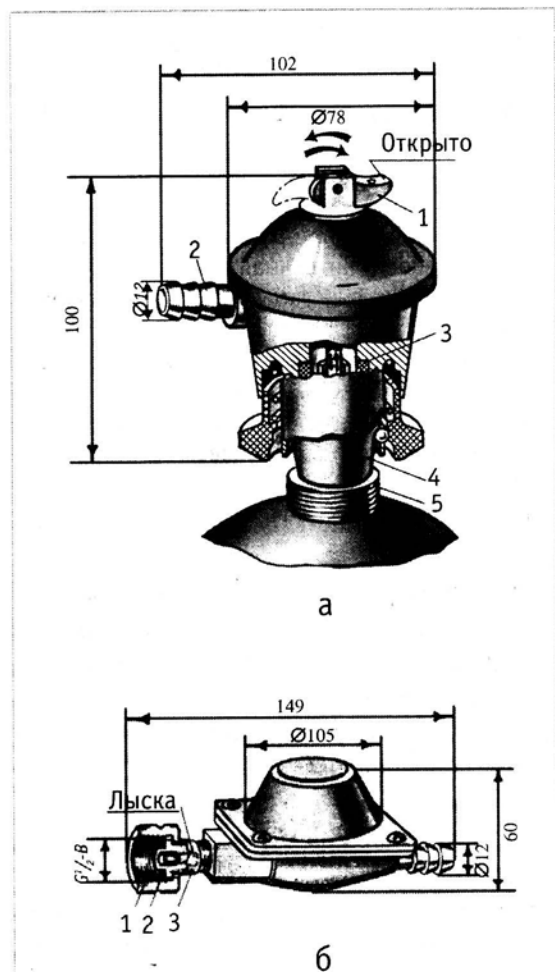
Регуляторы давления газа: а — РДСГ2-1,0 (Балтика) с клапаном на баллоне: 1 — рукоятка; 2 — штуцер; 3 — резиновое уплотнительное кольцо; 4 — клапан; 5 — резьбовая втулка баллона; б — РДСГ-1,2: 1 — накидная гайка с левой резьбой; 2 — прокладка; 3 — входной штуцер
